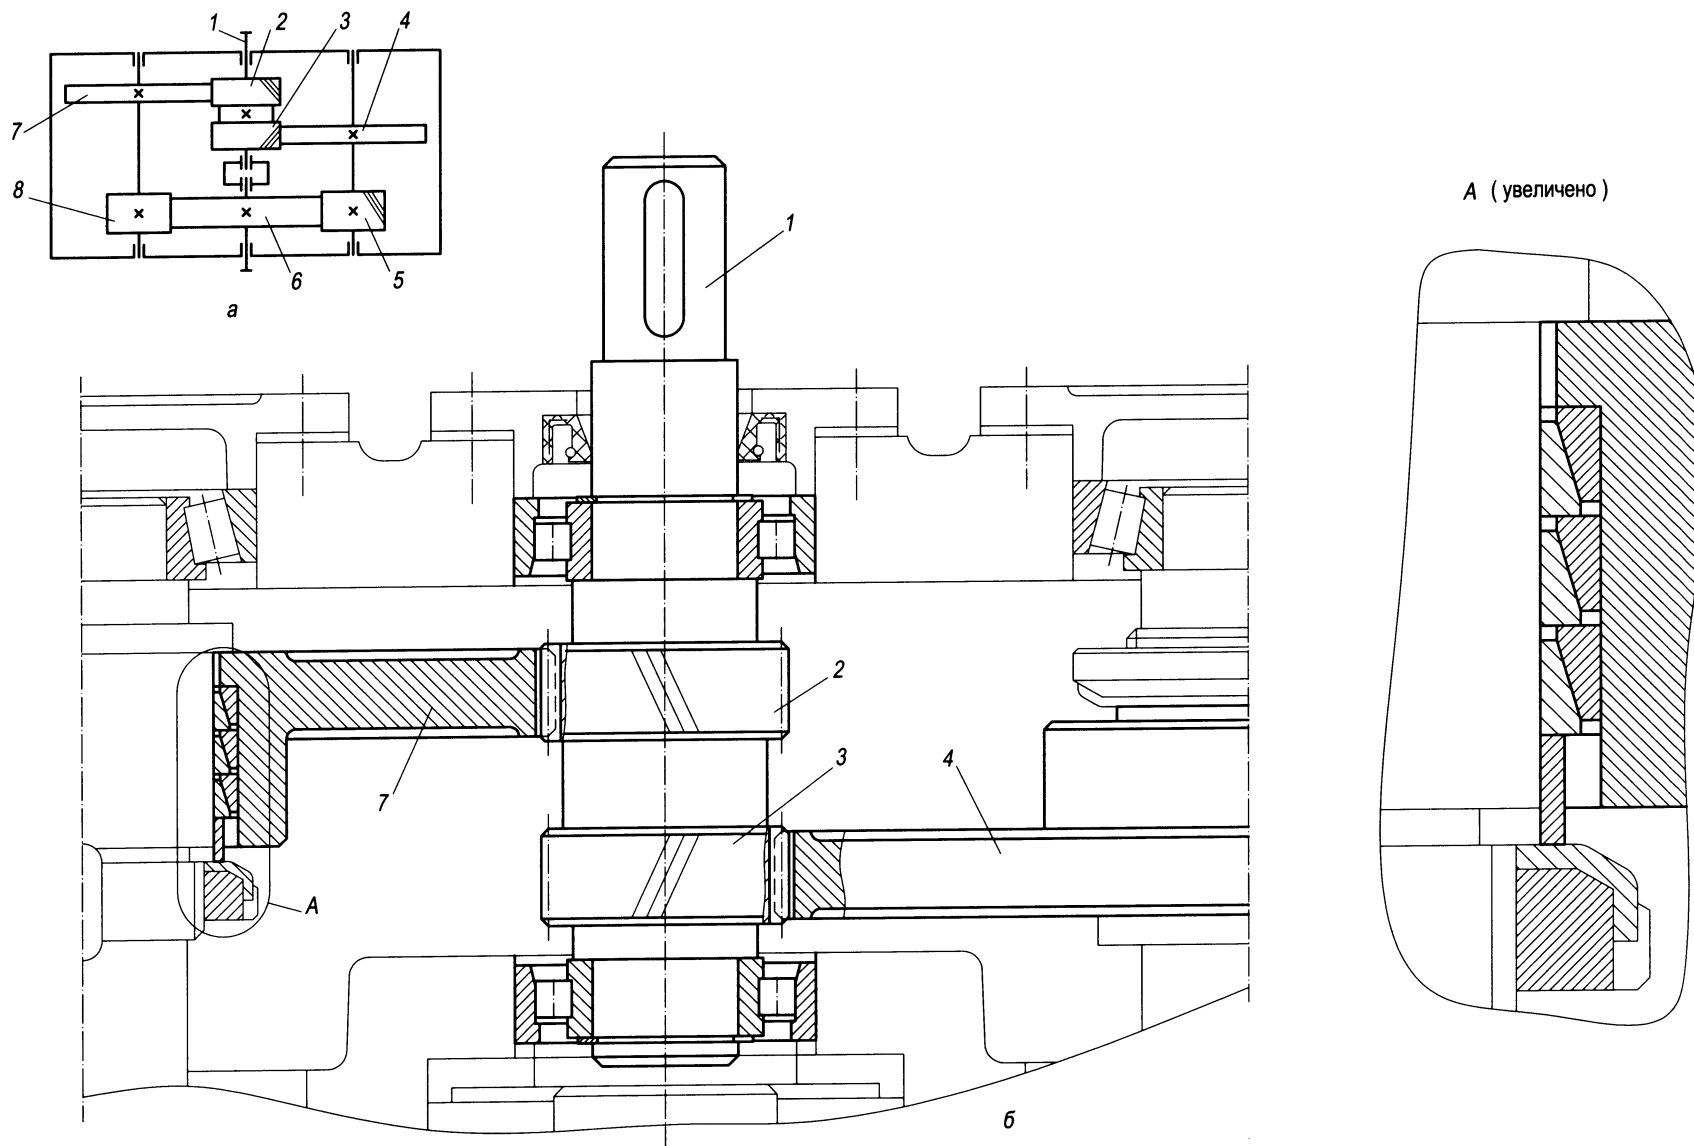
Кинематическая схема цилиндрического двухступенчатого двухпоточного редуктора (а) и эскиз быстроходного вала с шевронной передачей и плавающими опорами (б):
